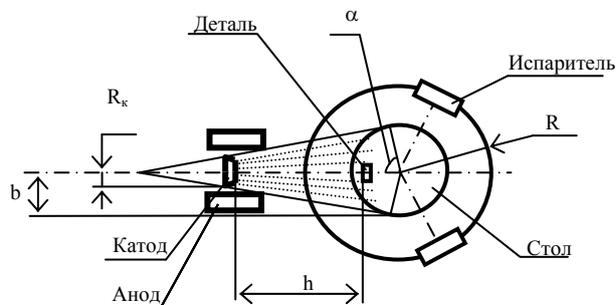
Схема расположения обрабатываемой детали относительно плазменного потока
